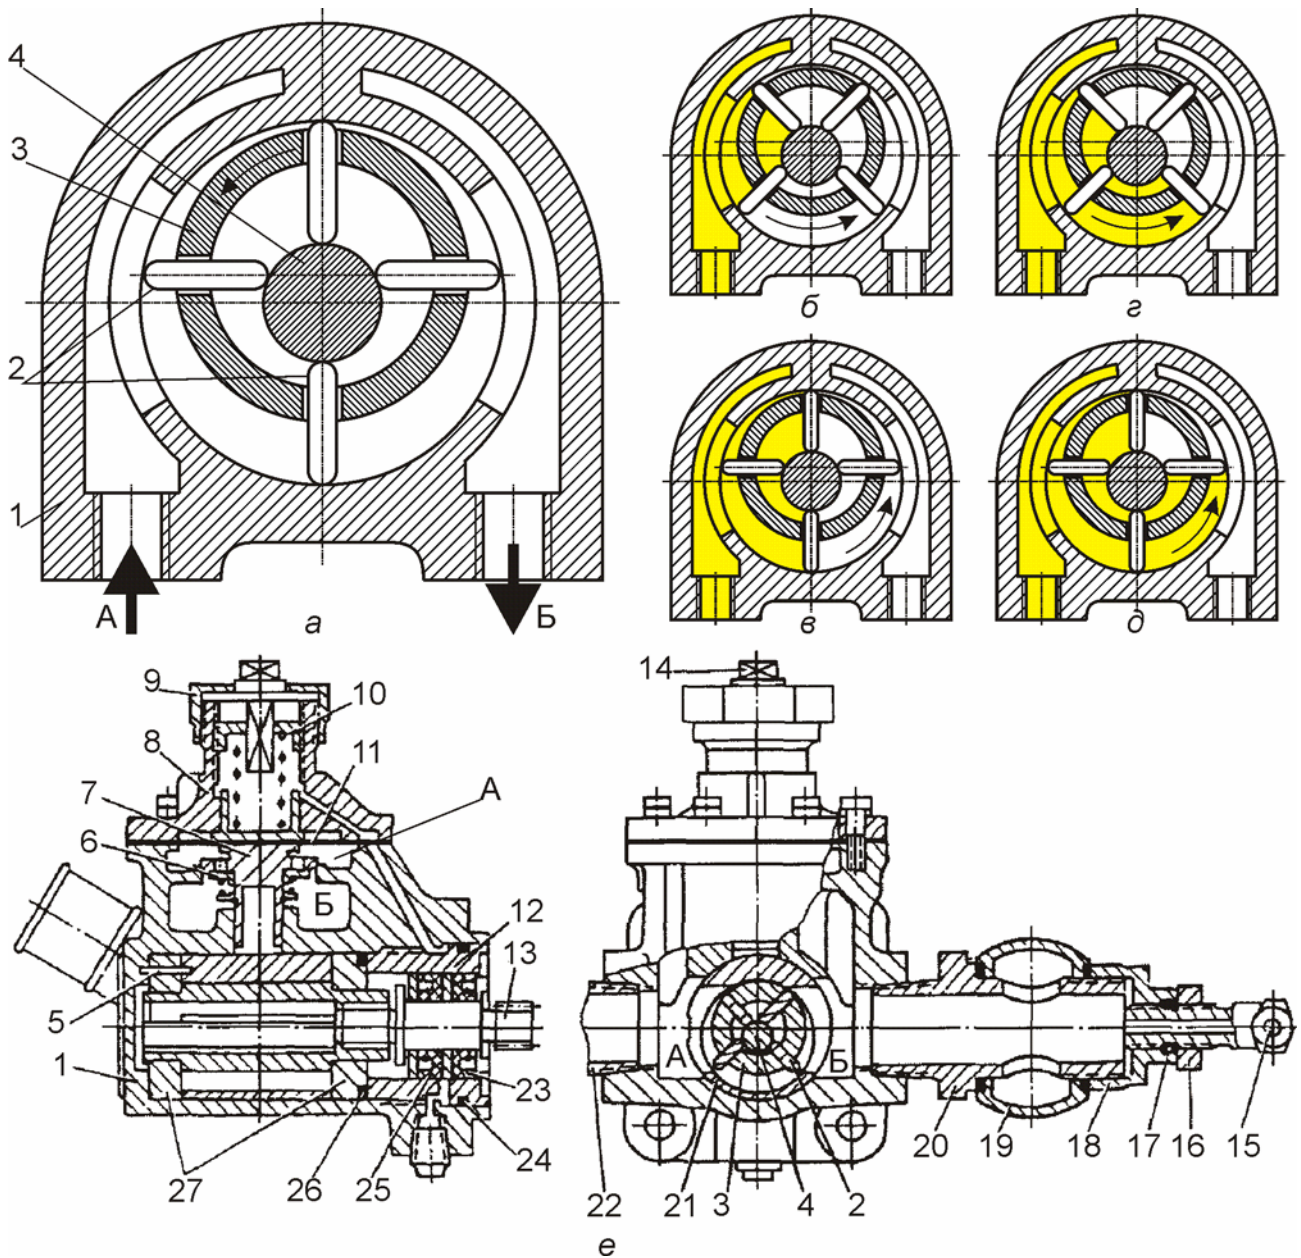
Коловоротний (пластинчастий) ПНД:
